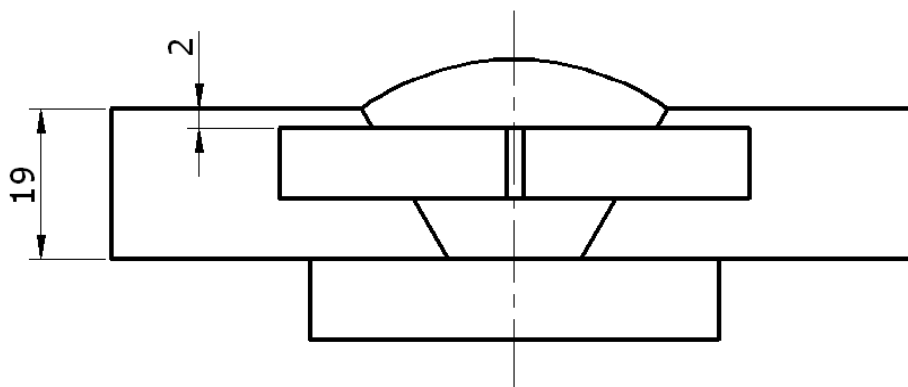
Posicionamento dos corpos-de-prova para ensaio de impacto Charpy-V em relação à junta soldada (cotas em mm).
